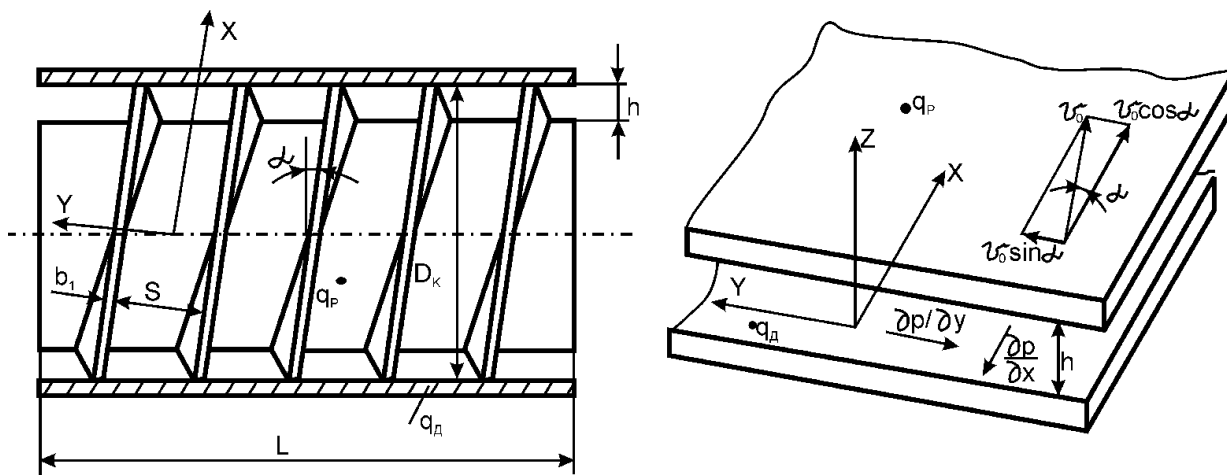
Конструктивна схема робочої частини шнекового електромеханічного гідролізера
